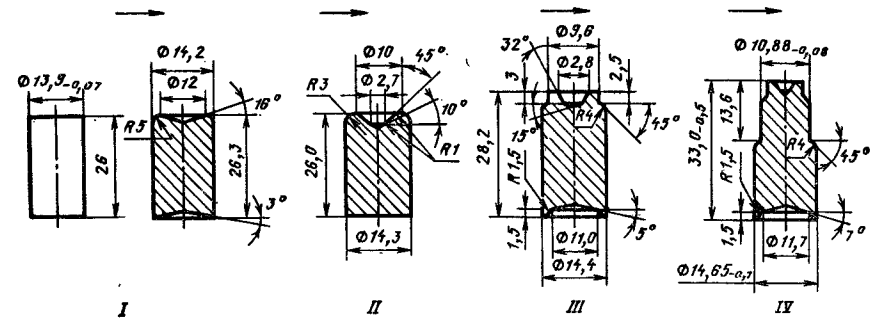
Технологический процесс штамповки заготовки наконечника гибкого шланга на четырехпозиционном автомате
